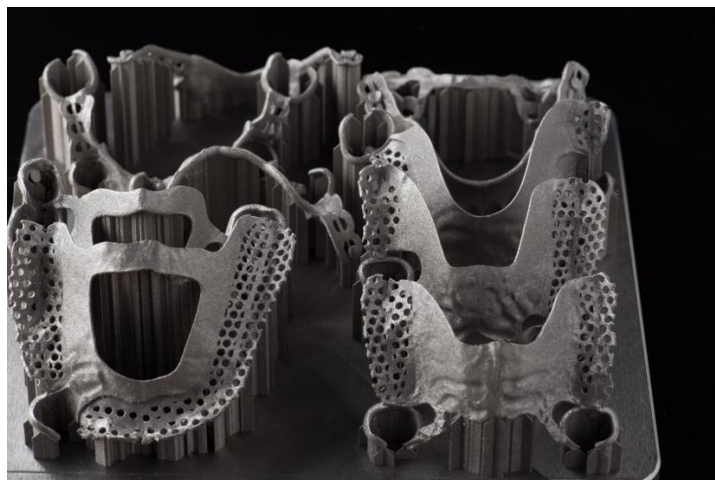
Fabrication additive de châssis métallique par technologies SLM
